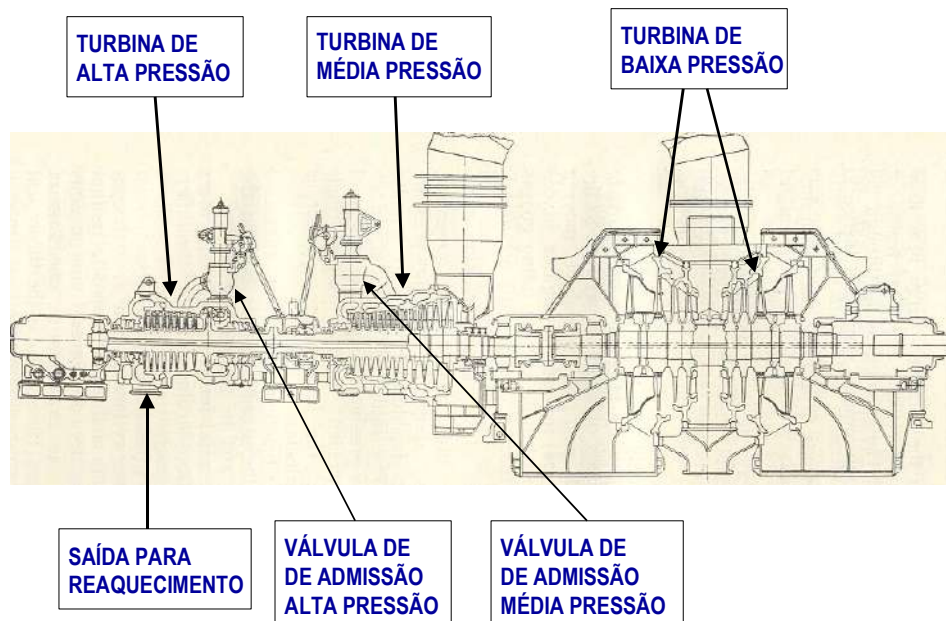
Vista em Corte de uma Turbina de Três Estágios com Reaquecimento
